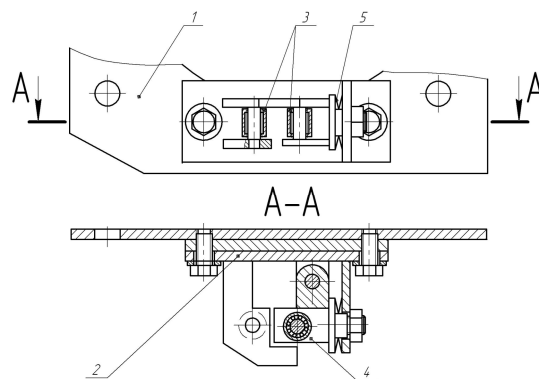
Фіксатор багатошпindelної головки для верстата з ЧПК
